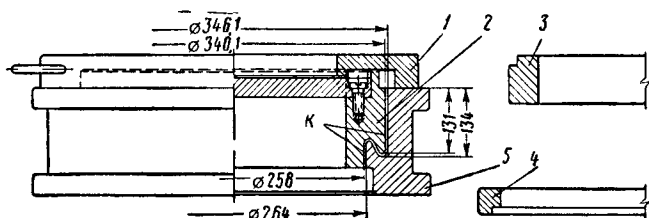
Прессформа для изготовления миканитовых манжет коллектора тягового двигателя ДК-103
